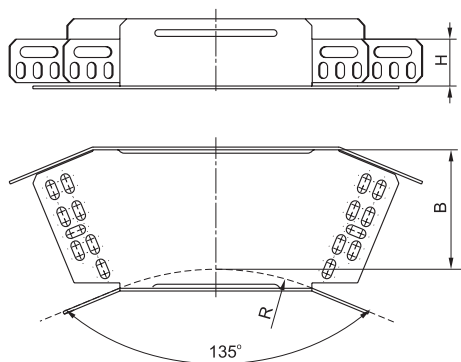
Поворот 45°. Размеры для размещения кабеля / Figure C.1 – 45° flat bend. Dimensions for cable placement
